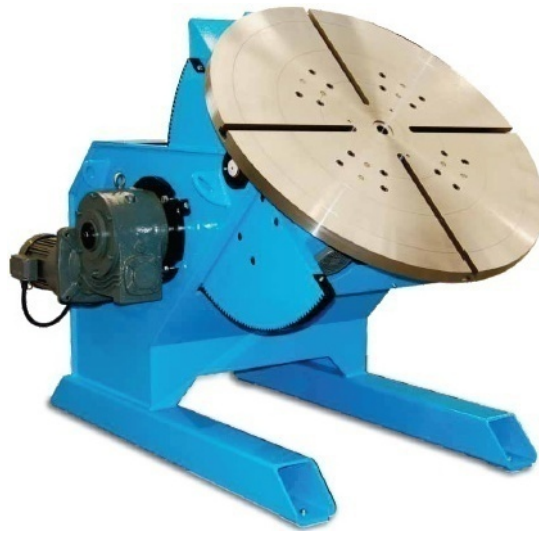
Сварочный вращатель РТ-1500
